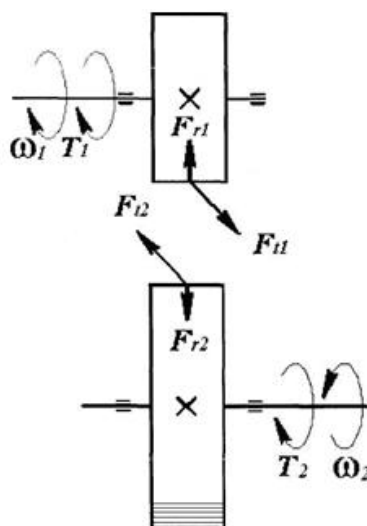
Схема сил в зацеплении зубчатой передачи редуктора [4]
